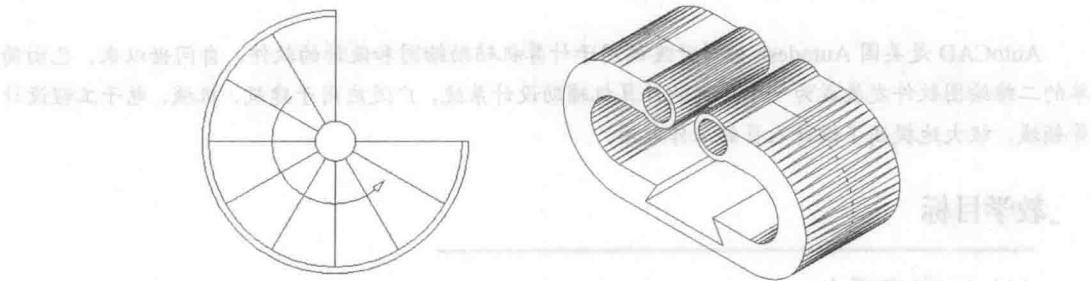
利用 AutoCAD 绘制的平面图形和三维图形
